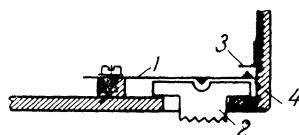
Выключатель питания: 1 — контактная пружина; 2 — ползунок; 3 — неподвижный контакт; 4 — корпус приемника
